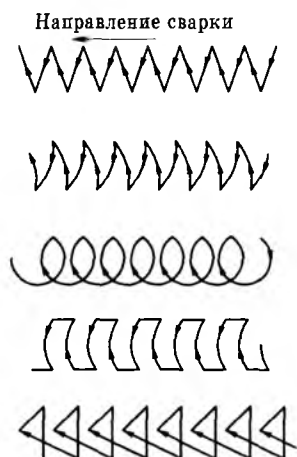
Схема движений электрода при ручной электродуговой сварке
